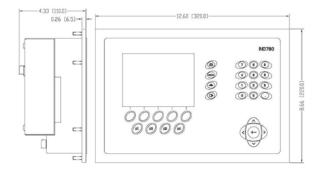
Dimensioni dell'armadietto con montaggio a pannello dell'IND780
